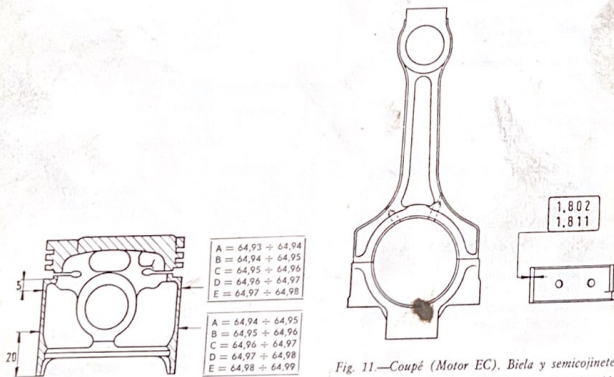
Coupé (motor EC). Dimensiones del pistón.
